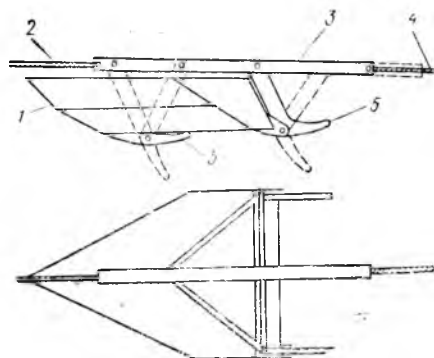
Схема устройства оборудования скреперного типа для разборки пыжа:
